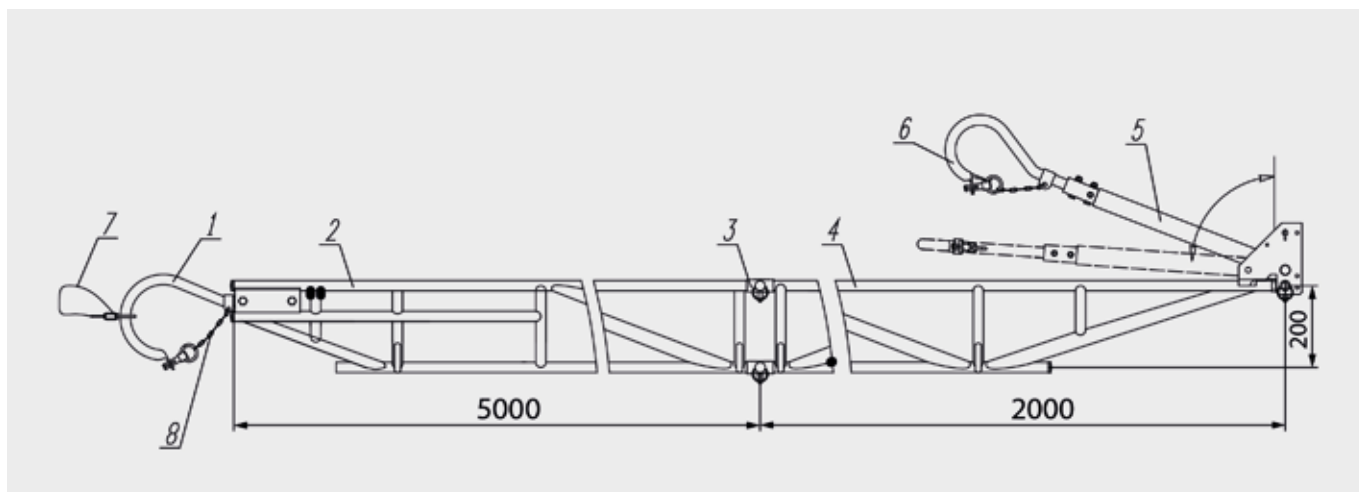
Трап ТРМЛ-0,3-5-2: 1 — крюк-захват; 2 — ферма основная (5 м); 3 — фиксатор; 4 — ферма дополнительная (2 м); 5 — подвес; 6 — захват или кабельный захват; 7 — строп цепной; 8 — замыкатель. Размеры указаны в миллиметрах
